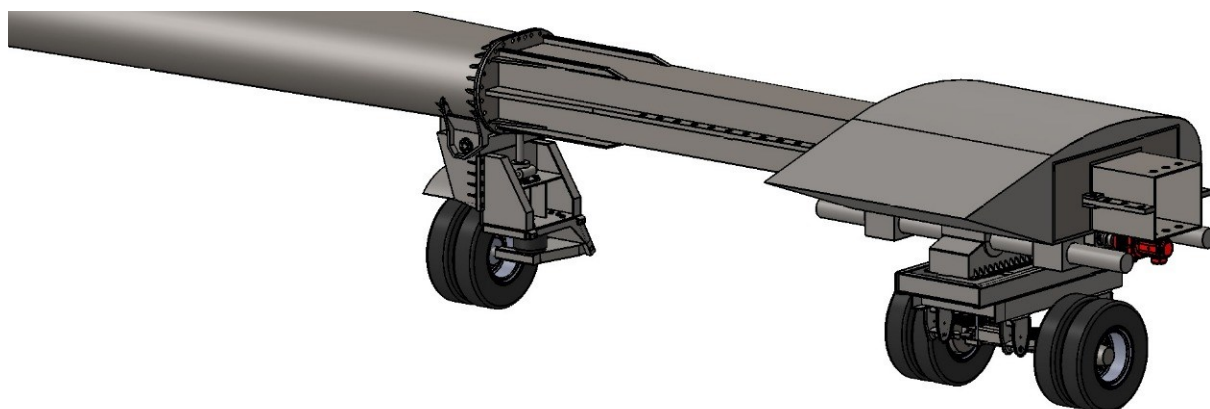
Base adaptadora para fixação de chassi com eixos simples, duplo ou triplo.
